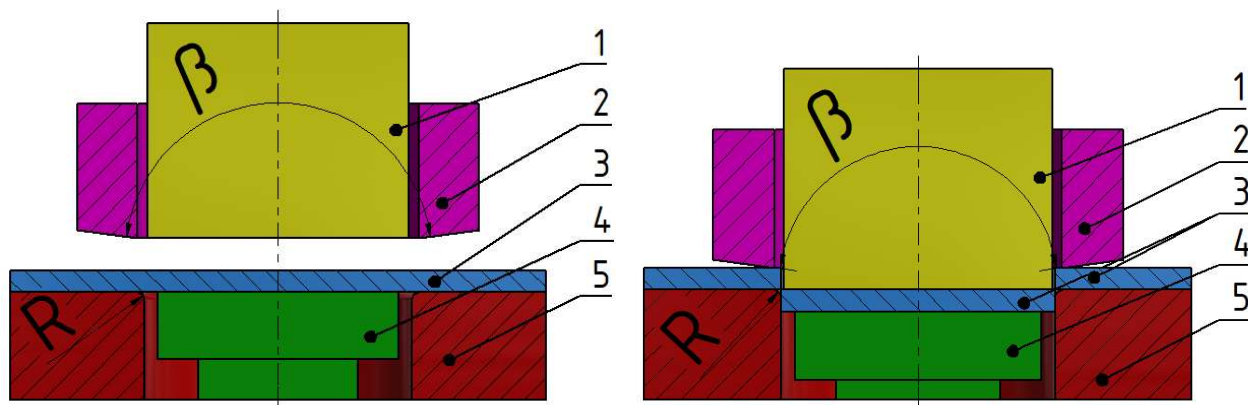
Děrování se zaoblenými střížnými hranami [2]
